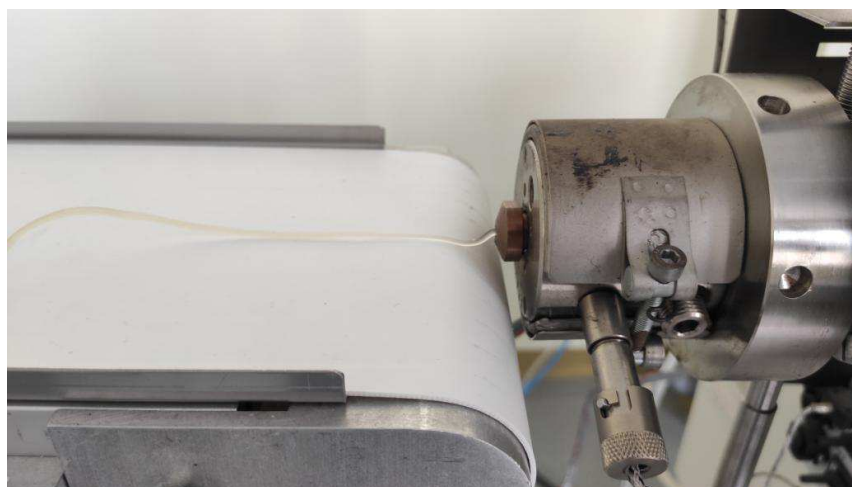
Выход полимерного прутка из сопла экструдера
